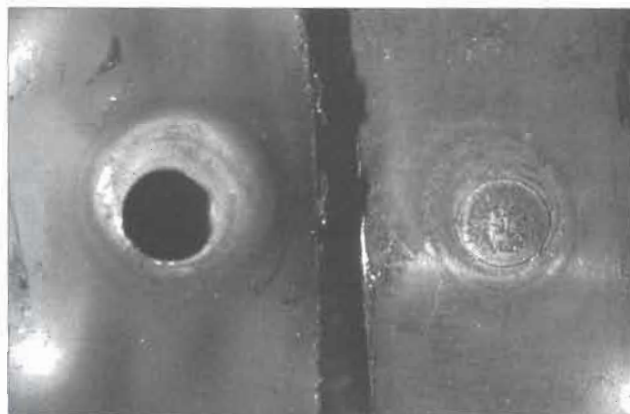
Внешний вид сварной точки с вырывом ее ядра
